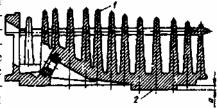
Головка цилиндров двигателя мотоциклов "Днепр-12" и K-750M
